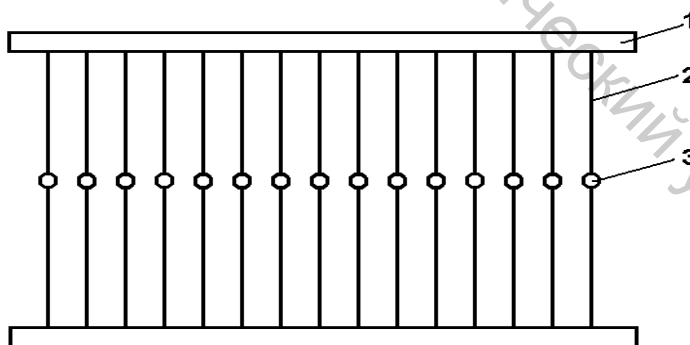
Деталь ткацкого станка (ремизка): 1 – рейка; 2 – галево; 3 – глазок
